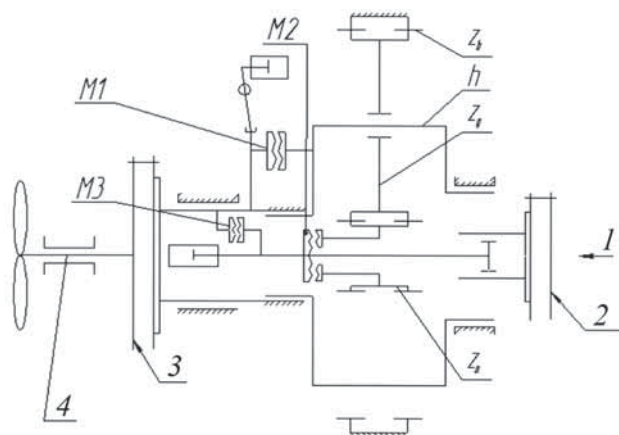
Кинематическая схема планетарного редуктора: 1 — вход от электродвигателя; 2 — эластичная муфта 1; 3 — эластичная муфта 2; 4 — судовой валопровод
